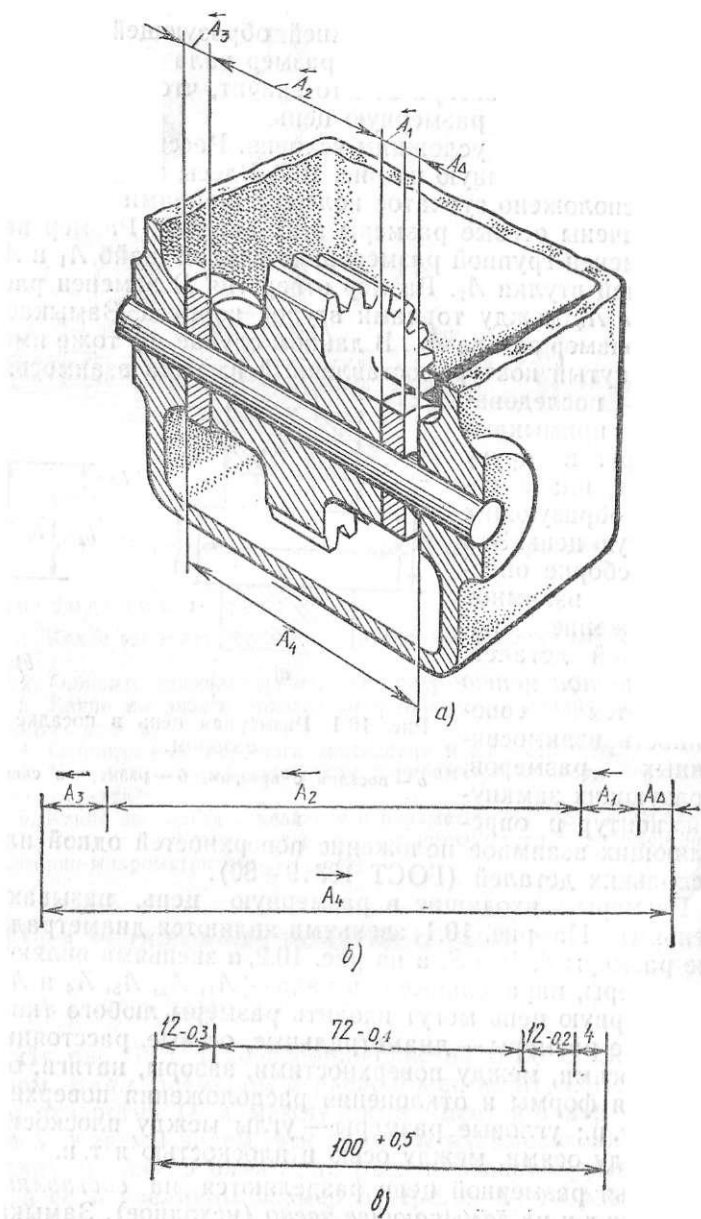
Размерная цепь в редукторе (а), схема размерной цепи редуктора (б) и размеры звеньев (в)
